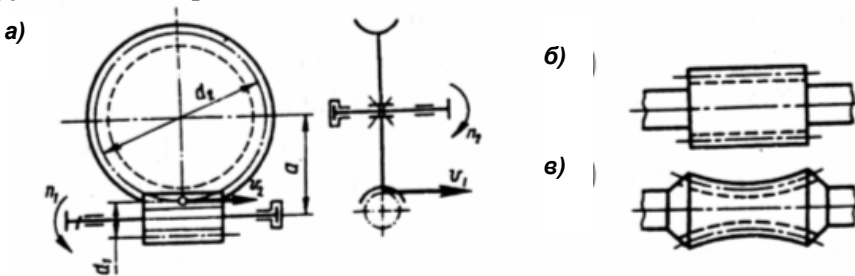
Схема червячной передачи лифтового редуктора: а - червячная передача; б - червяк цилиндрический; в - червяк глобоидный
